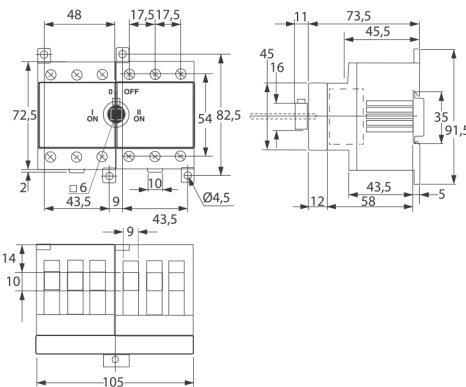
Габаритные и установочные размеры реверсивных рубильников 40-80А
